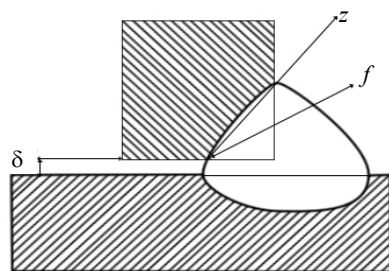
Поперечное сечение углового шва в тавровом соединении
